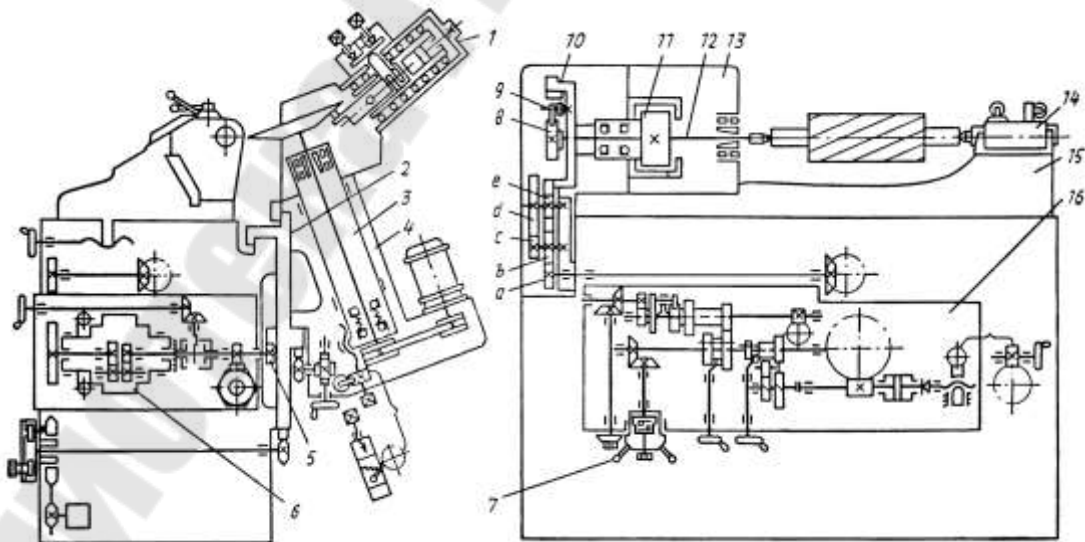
Кинематическая схема полуавтомата модели 3А622 для заточки червячных фрез: 1 – механизм правки; 2 – шлифовальные салазки; 3 – шлифовальная головка; 4 – шлифовальная бабка; 5 – реечная шестерня; 6 – дифференциал; 7 – маховичок; 8 – делительный диск; 9 – фиксатор; 10 – шестерня; 11 – гидродвигатель; 12 – шпиндель изделия; 13 – бабка изделия; 14 – задняя бабка; 15 – поперечные салазки; 16 – механизм подачи и спиралеобразования
